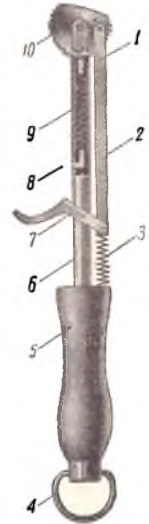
Искровая подвесная зажигалка для газа в виде рукоятки: 1 — кремь; 2 — тяга; 3 — возвратная пружина; 4 — кольцо для подвешивания; 5 — рукоятка; 6 — трубка пружины кремня; 7 — курок; 8 — регулятор пружины; 9 — пружина кремня; 10 — огниво
